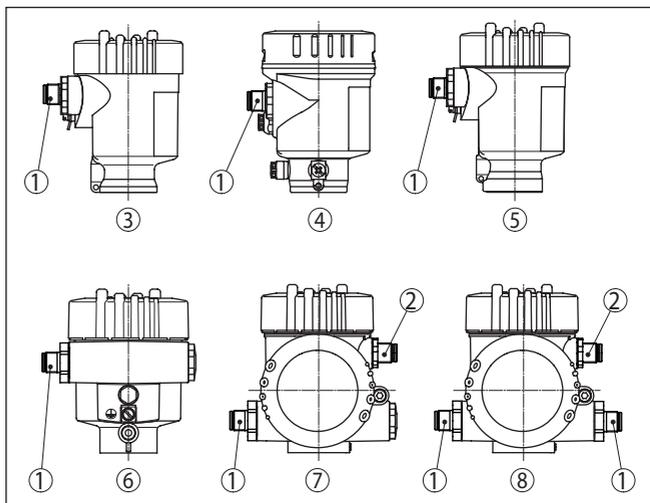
Положение штекерного разъема в разных исполнениях корпуса
